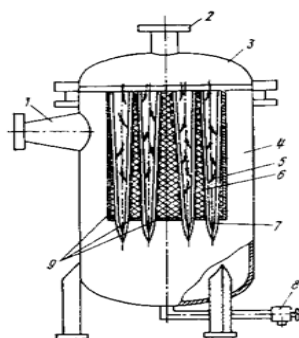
Конструкція фільтра–сепаратора СТ–500–2: 1–вихідний патрубок; 2–патрубок входу; 3–кришка; 4–корпус; 5– фільтрувальний чохол; 6– водовіддільний чохол; 7–шлейфи; 8–патрубок сливу; 9–каркас
